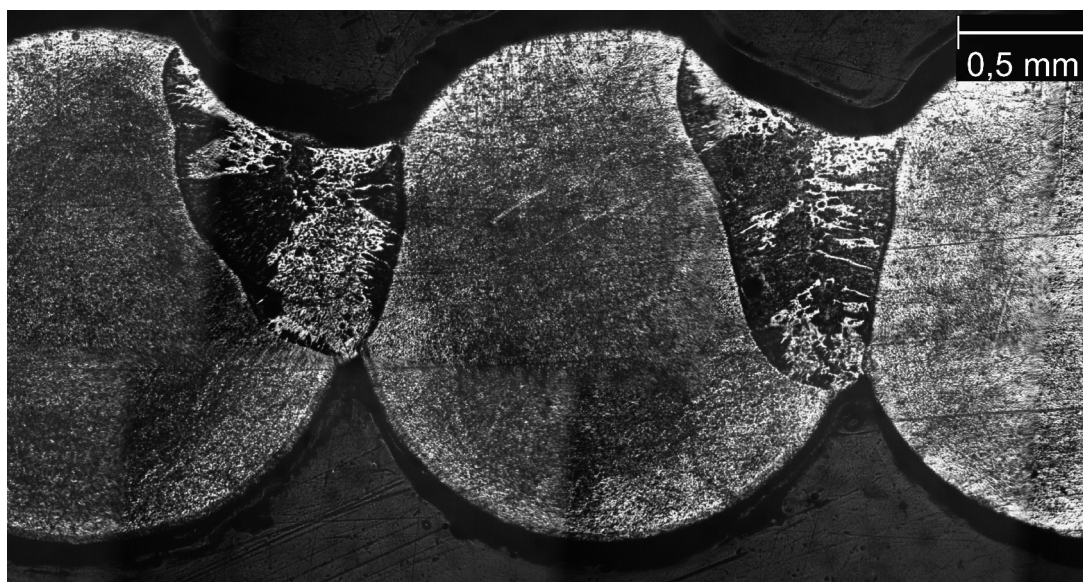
Общий вид области сварного шва пружинно-витого канала, полученного сваркой непрерывным лазерным излучением
